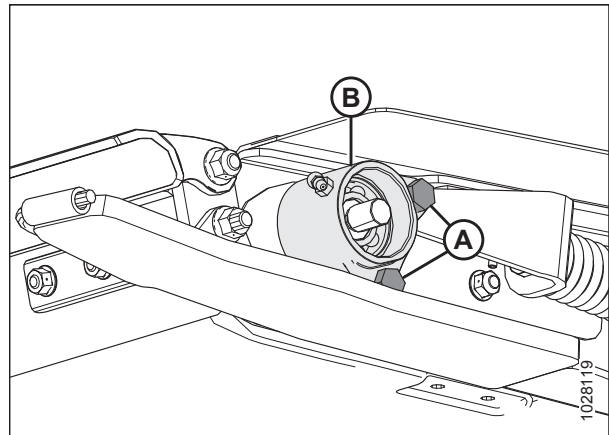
Carcasa del rodamiento del rodillo tensor
